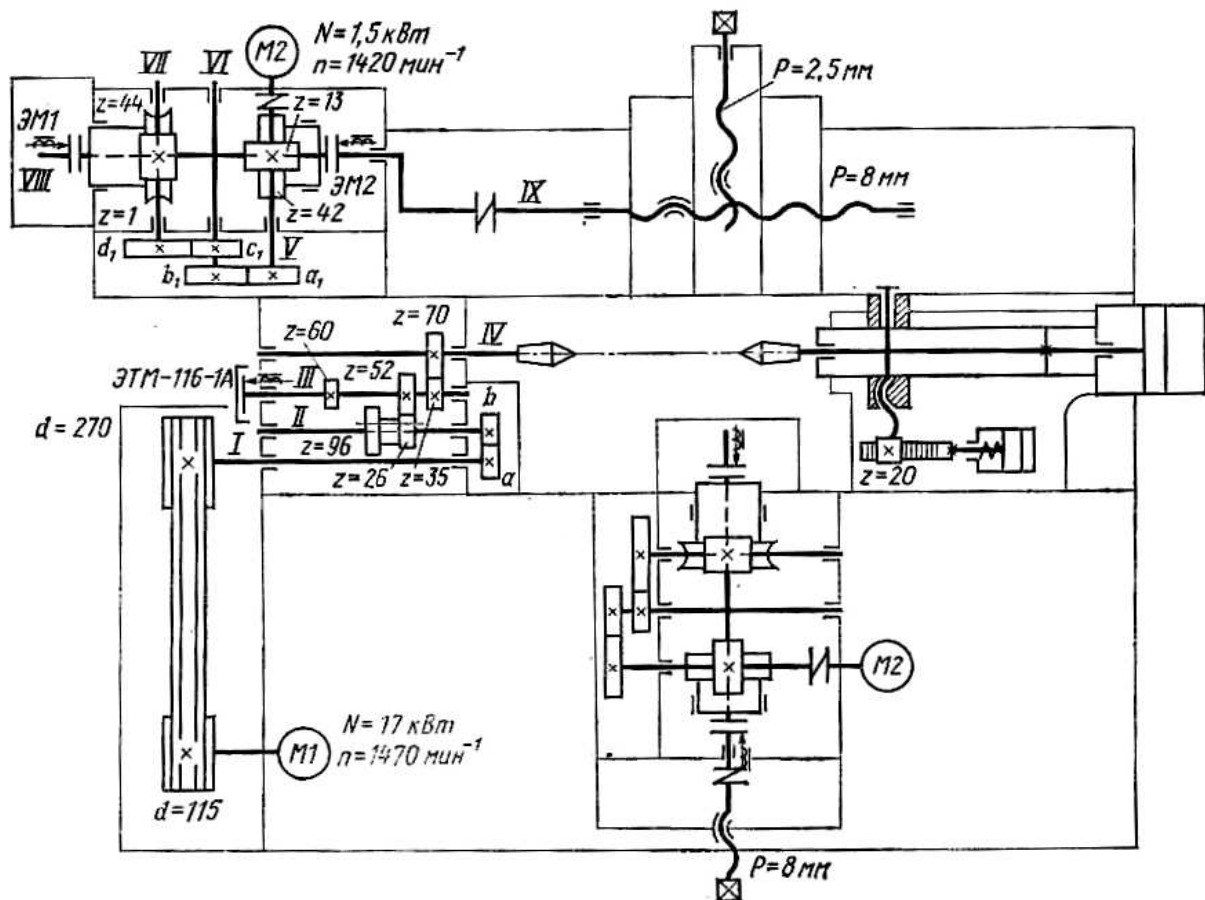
Кинематическая схема многолезцового полуавтомата
